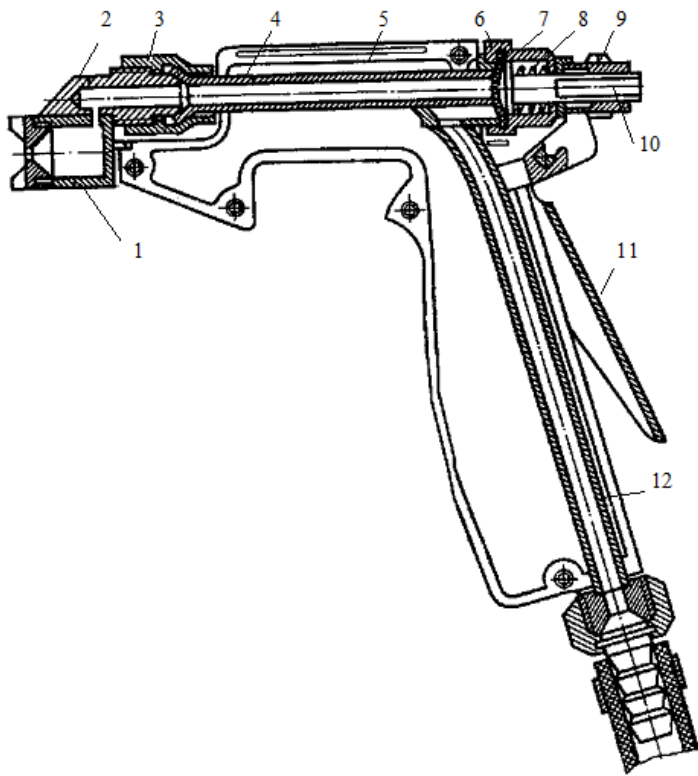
Центробежный распылитель красок: 1 – головка; 2 – штуцер; 3 – гайка; 4 – трубка; 5 – корпус; 6 – крышка; 7 – диафрагма; 8 – пружина; 9 – регулировочная гайка; 10 – шток; 11 – курок; 12 – рукоятка
